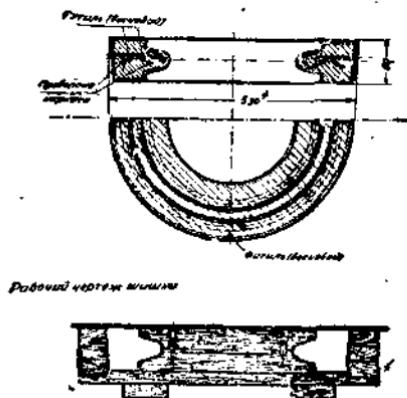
Изготовление кольцевой шишки для канатного ролика.
